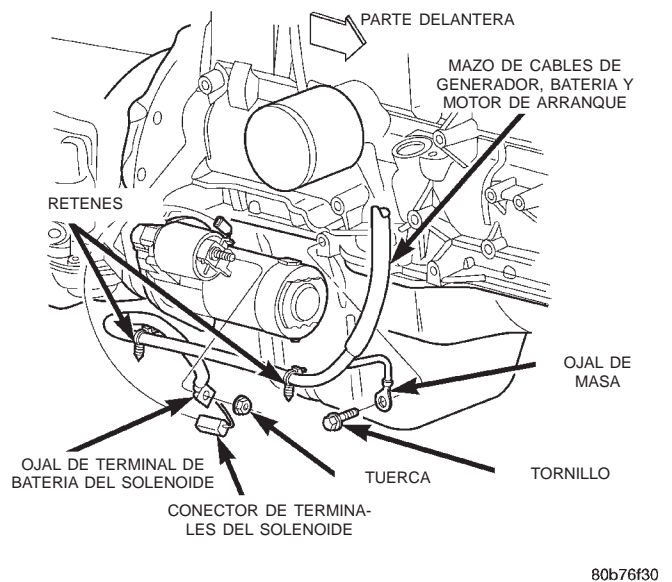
Desmontaje e instalación de mazos de cables del motor de arranque-motor 4.0L
